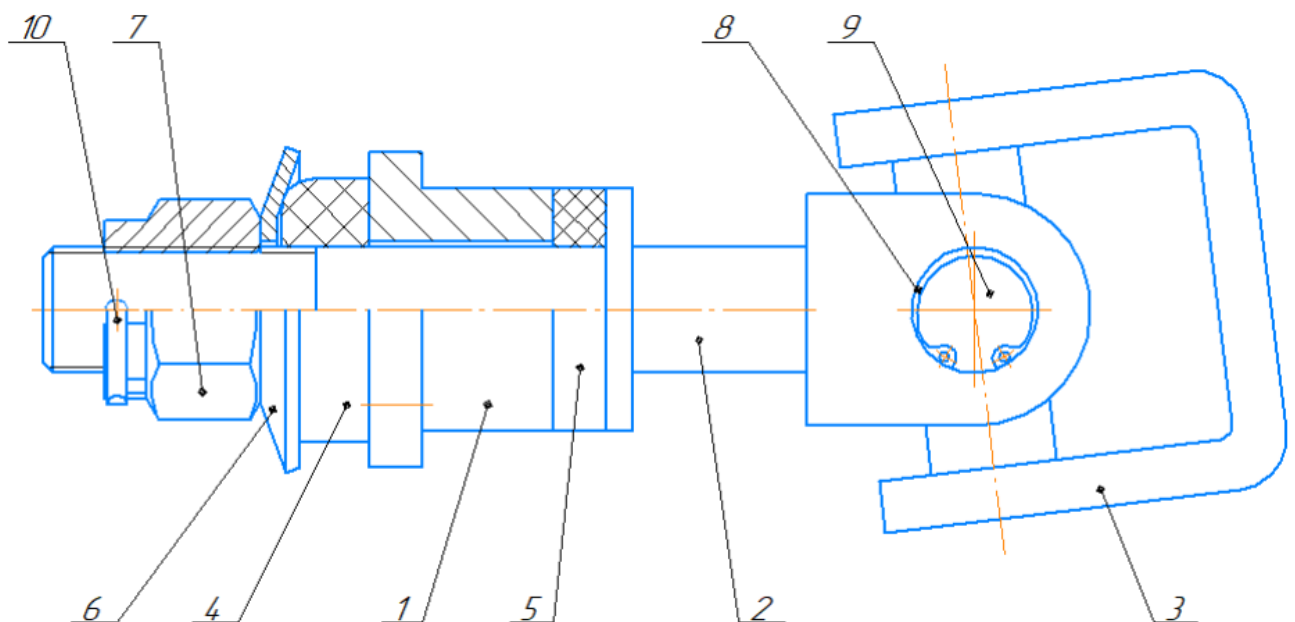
Стабілізуючий тягово-зчіпний пристрій: 1 - корпус пристрою; 2 - шток з передньою вилкою; 3 - задня вилка; 4 - гумовий демпфер; 5 - гумове кільце; 6 - притискна шайба; 7 - корончаста гайка; 8 - стопорне кільце; 9 - хрестовина; 10 - шплінт.
